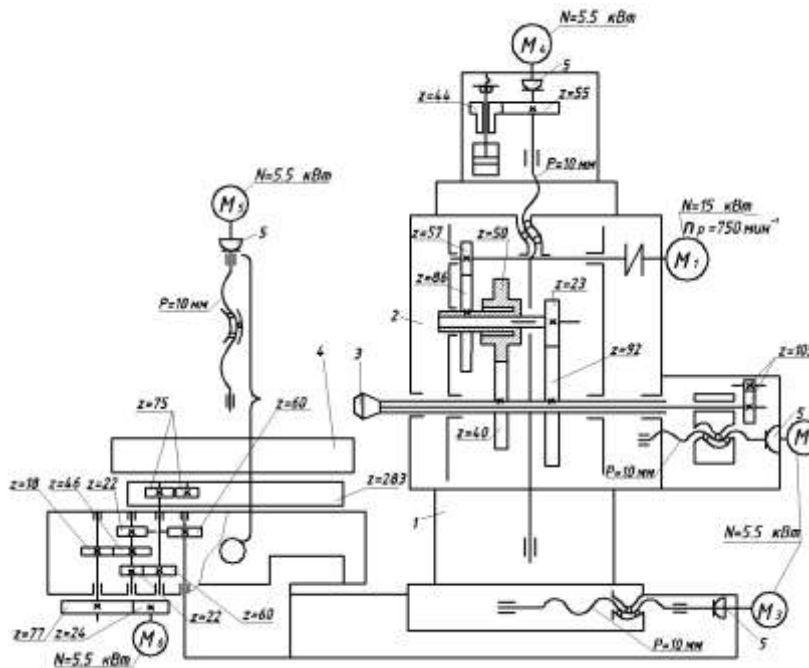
Кинематическая схема станка мод. 2623ПМФ4
